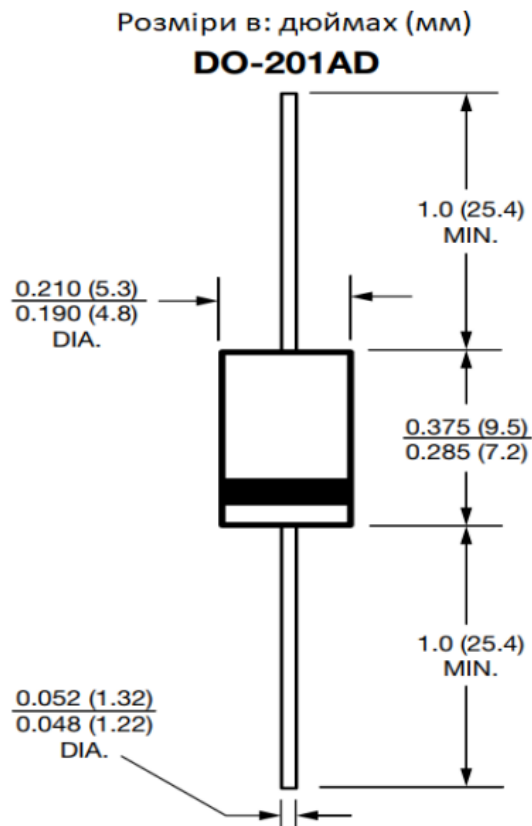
Зовнішній вигляд і розміри корпусу діода 1N5403 [9]
